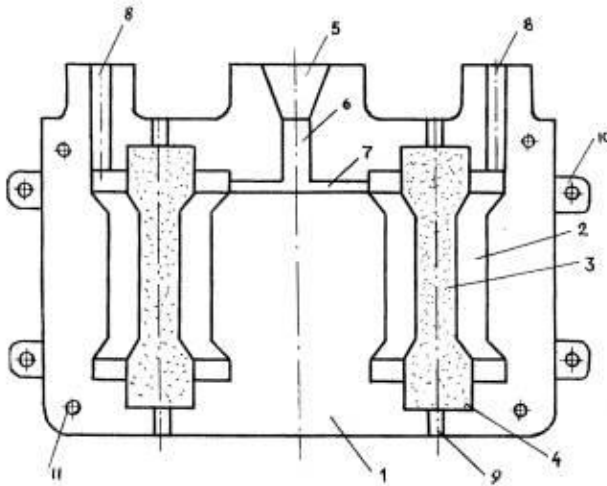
Эскиз сечения собранной металлической формы – кокиля:
